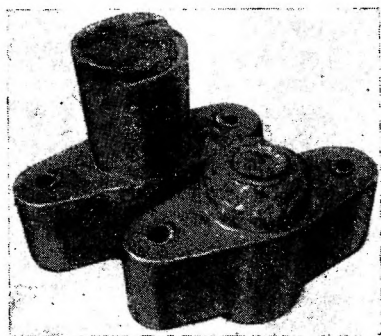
Форма вставки, изготовленной из экзотермической смеси, для прибылей цилиндрической формы.
